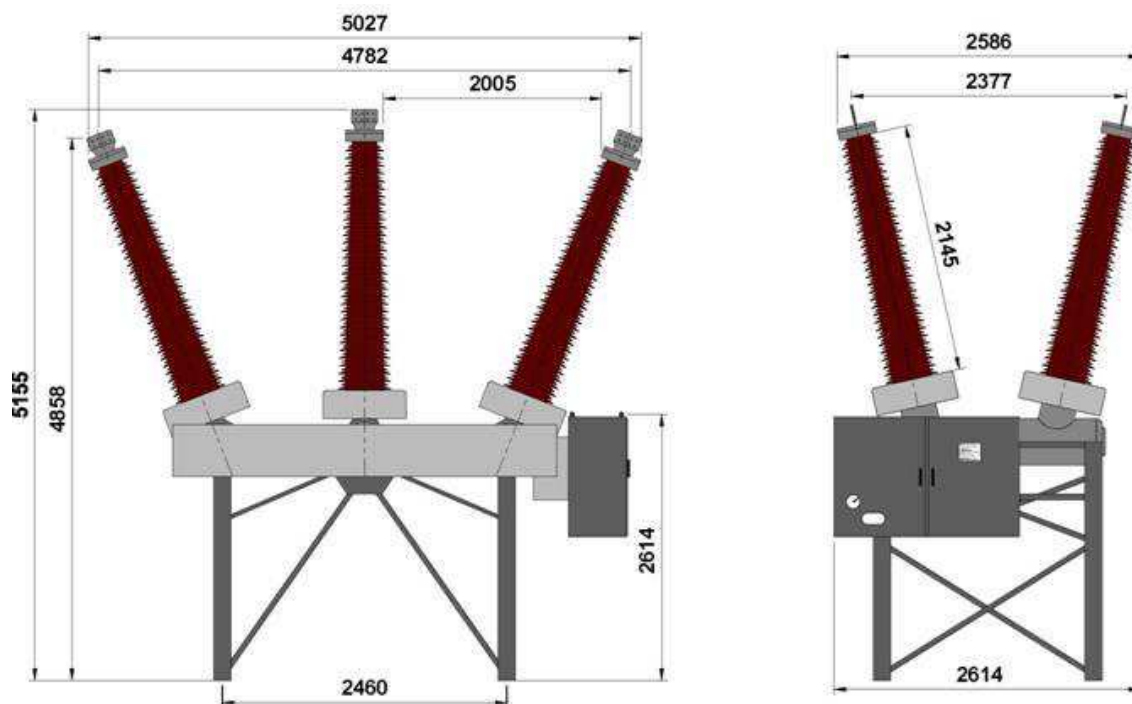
Внешний вид и габаритные размеры выключателя 220 кВ
